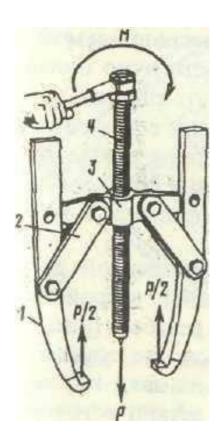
Винтовой съемник с лапчатыми захватами: 1 — захват, 2 — тяга; 3 — корпус; 4 — силовой винт
